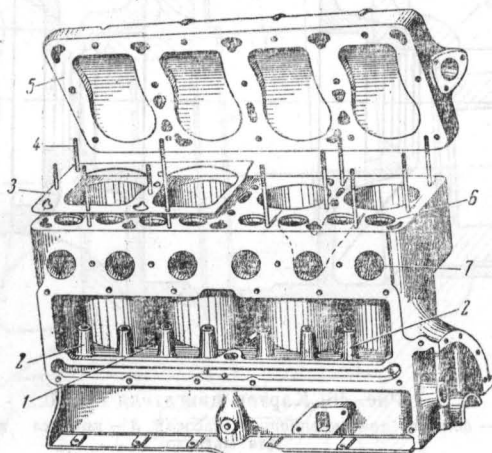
Блок цилиндров двигателя ГАЗ-МК:
